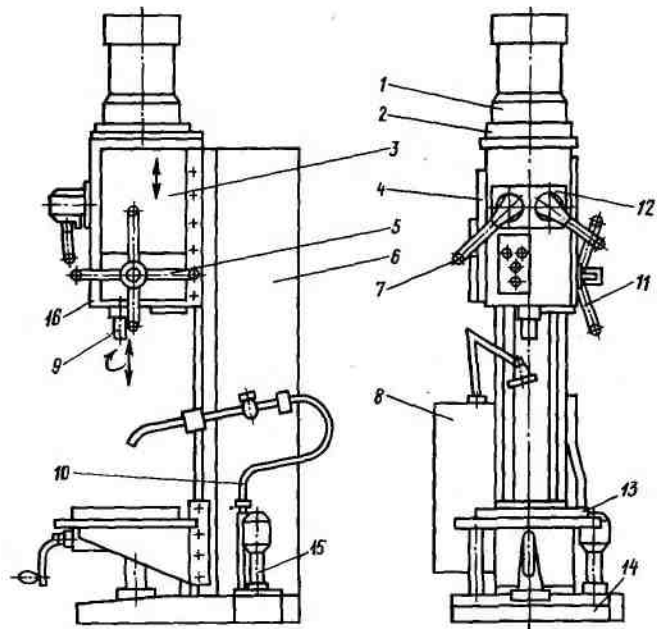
Общий вид вертикально-сверлильного станка мод. 2H135:
